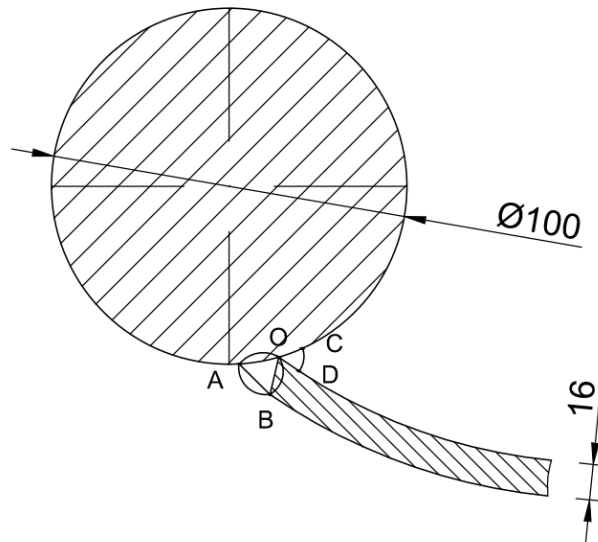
Конструктивний розріз зварного шву нестандартної конфігурації.
